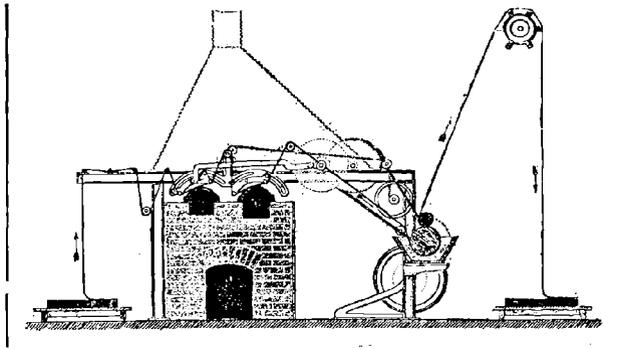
Machine à griller à la plaque avec dispositif modifiant le contact de l'étoffe pour ne pas refroidir les plaques.
